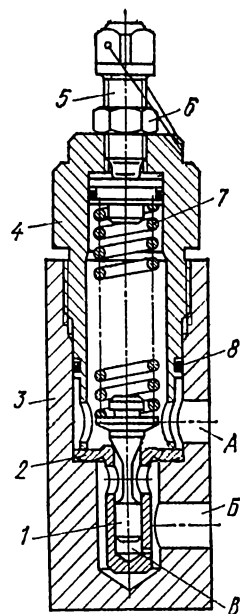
Схема конусного предохранительного клапана прямого действия с гайкой:
